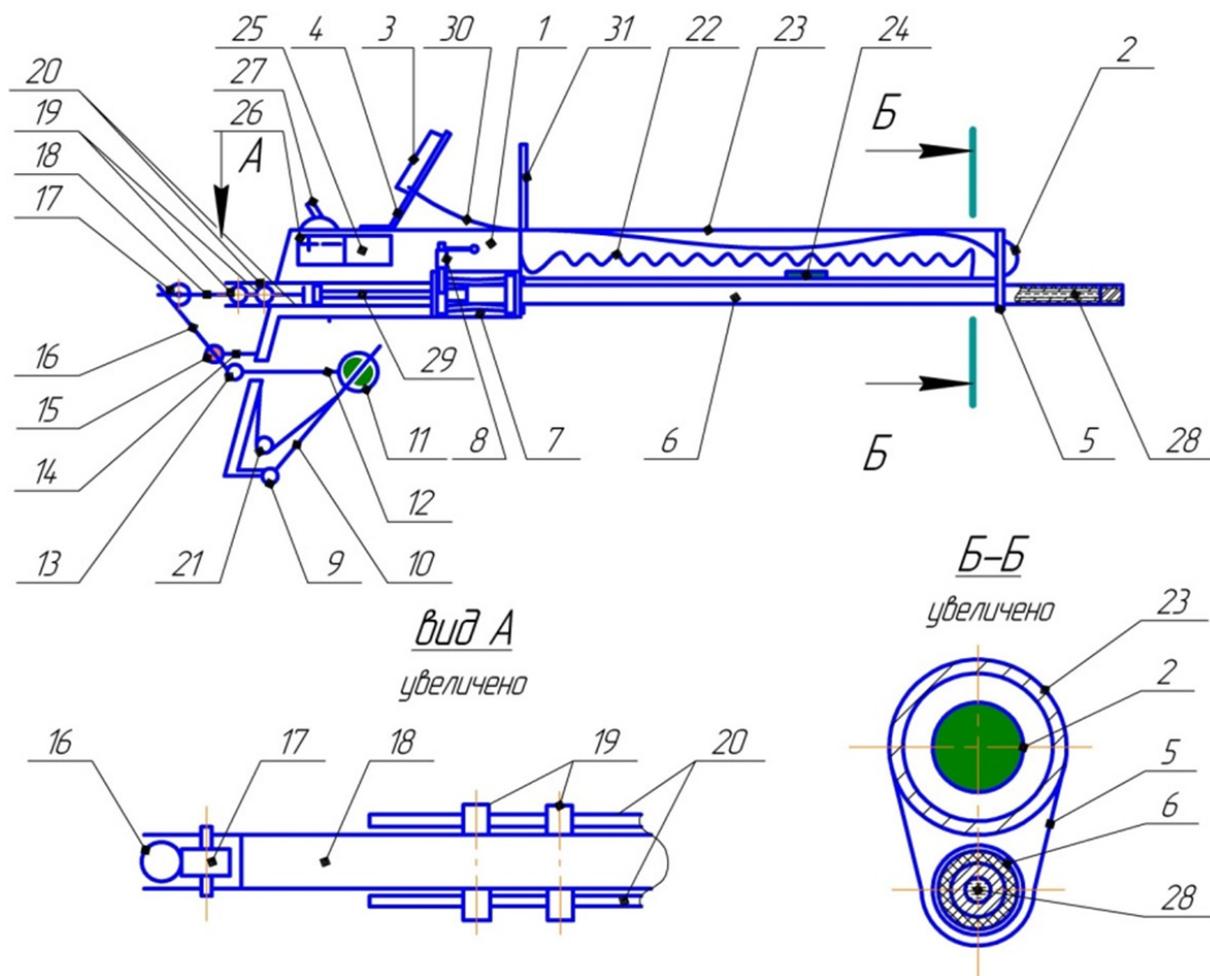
Схема аппарата для искусственного осеменения: 1 – корпус; 2 – мини-видеокамера; 3 – мобильный телефон; 4 – кронштейн; 5 – заглушка; 6 – шприц осеменатора; 7 – посадочное место под шприц; 8 – фиксатор; 9 – шарнир; 10 – кулиса; 11 – шарнир-ползун; 12 – шатун; 13 – шарнир; 14 – кронштейн; 15 – ось; 16 – рычаг; 17 – ролик; 18 – толкатель; 19 – бобышки; 20 – направляющая; 21 – возвратная пружина; 22 – нагреватель; 23 – трубка; 24 – датчик температуры; 25 – терморегулятор; 26 – батарея питания; 27 – выключатель; 28 – порция семени; 29 – поршень; 30 – кабель; 31 – упор
